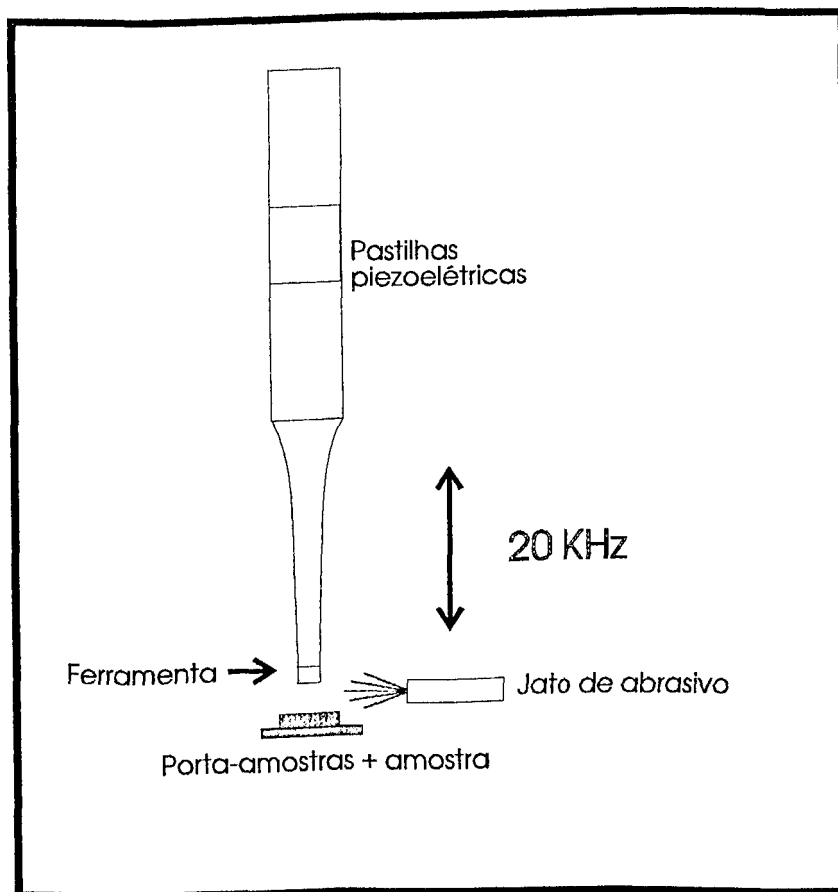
Representação esquemática do processo de usinagem por abrasão ultrassônica.
